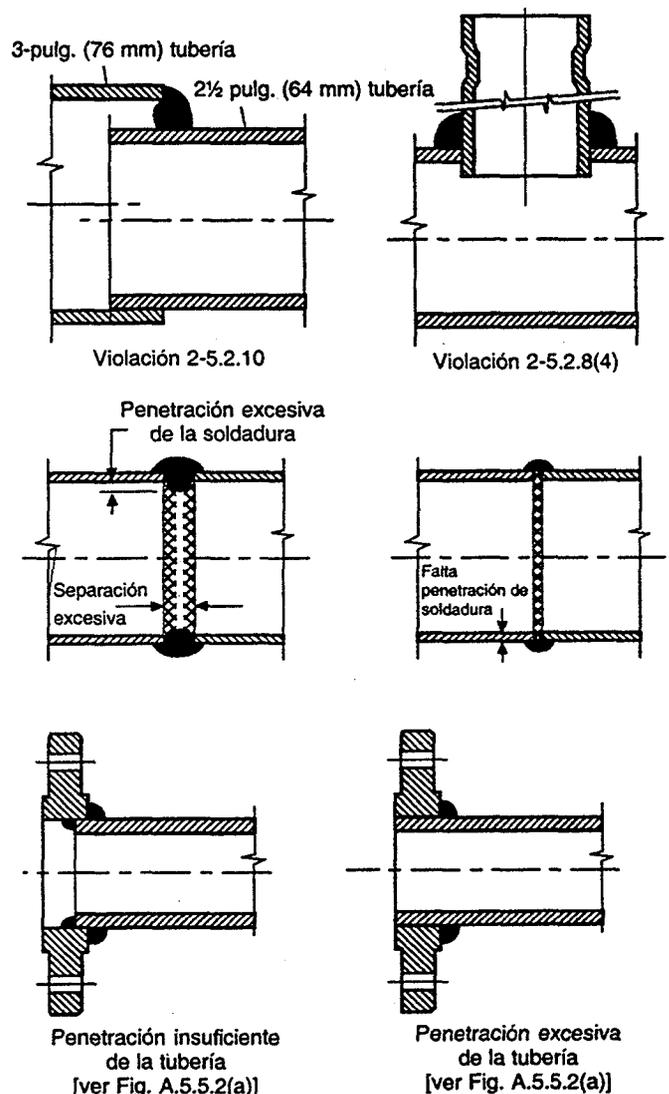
(b) Juntas soldadas no aceptables
